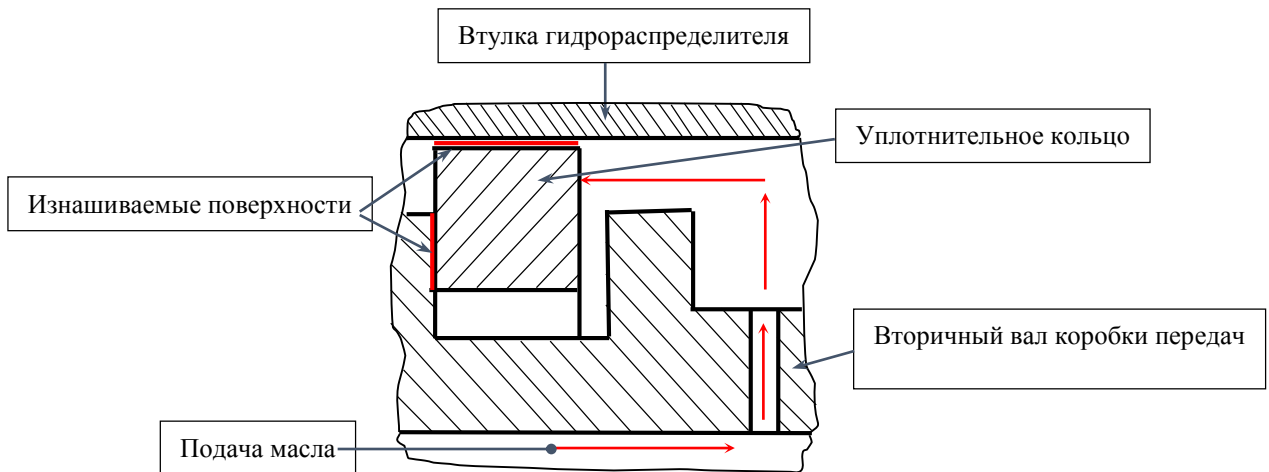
Схема износа уплотнительных колец гидрораспределителя коробки передач трактора типа Т-150К
